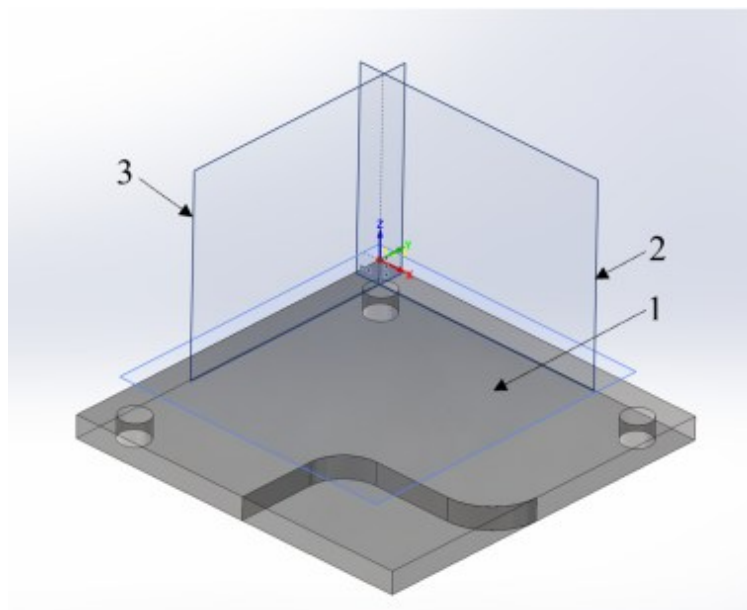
Прив'язка системи координат до заготовки та деталі
